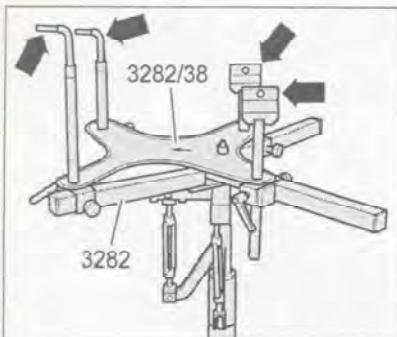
Установите выверочную доску 3282/38 на приспособление для крепления коробки передач 3282. Отрегулируйте положение приспособления для крепления коробки передач 3282 в соответствии с отверстиями на выверочной доске. Закрепите вертикальные элементы (стрелки) указанным образом.
